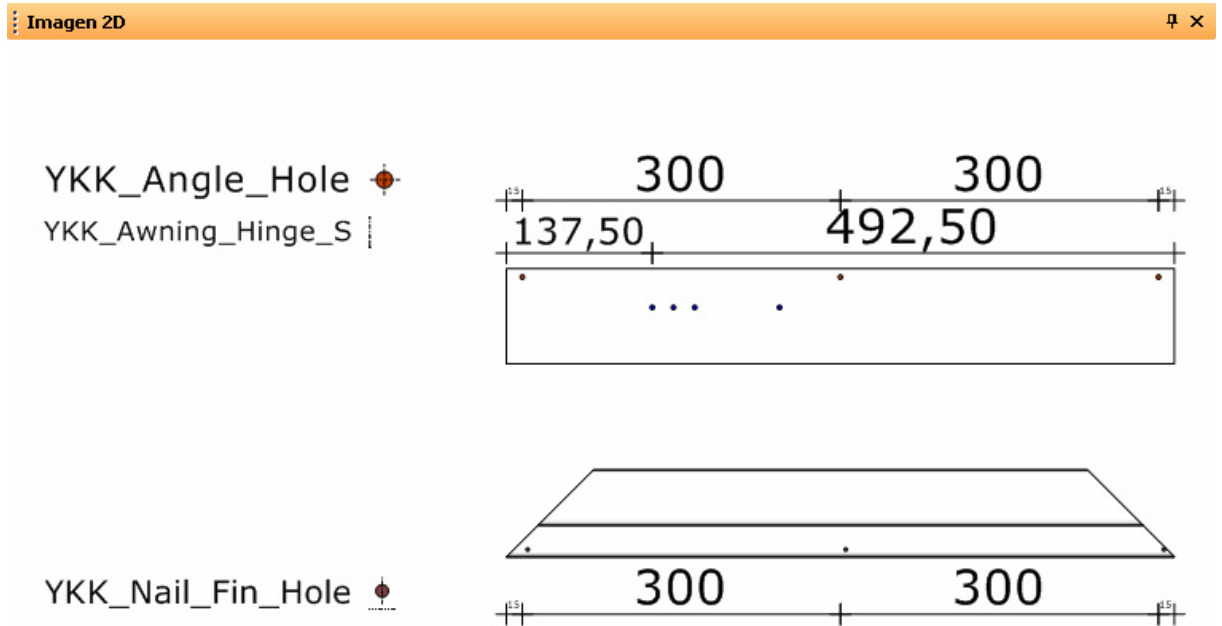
Planta (parte superior) y Alzado del perfil junto con sus operaciones.
